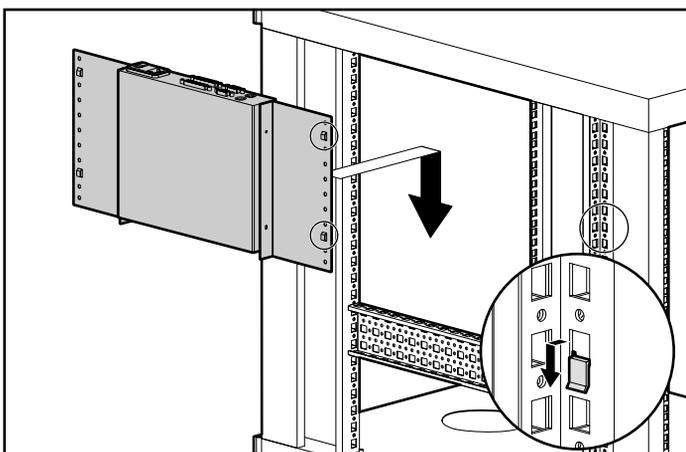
Montaggio dell'unità a 2 porte sulla parete laterale del rack
